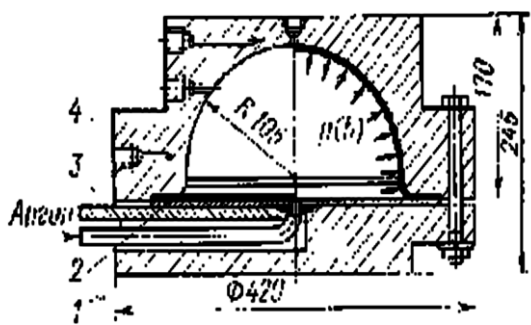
Штамп для формовки полусфер из титановых сплавов:1 – крышка; 2 – двухслойная заготовка; 3 – задвижка; 4 – матрица.
